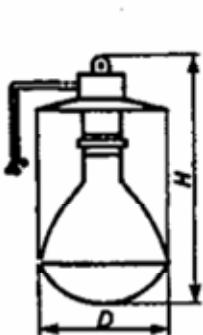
Внешний вид облучателя серии ОТ-1000МИ-049
